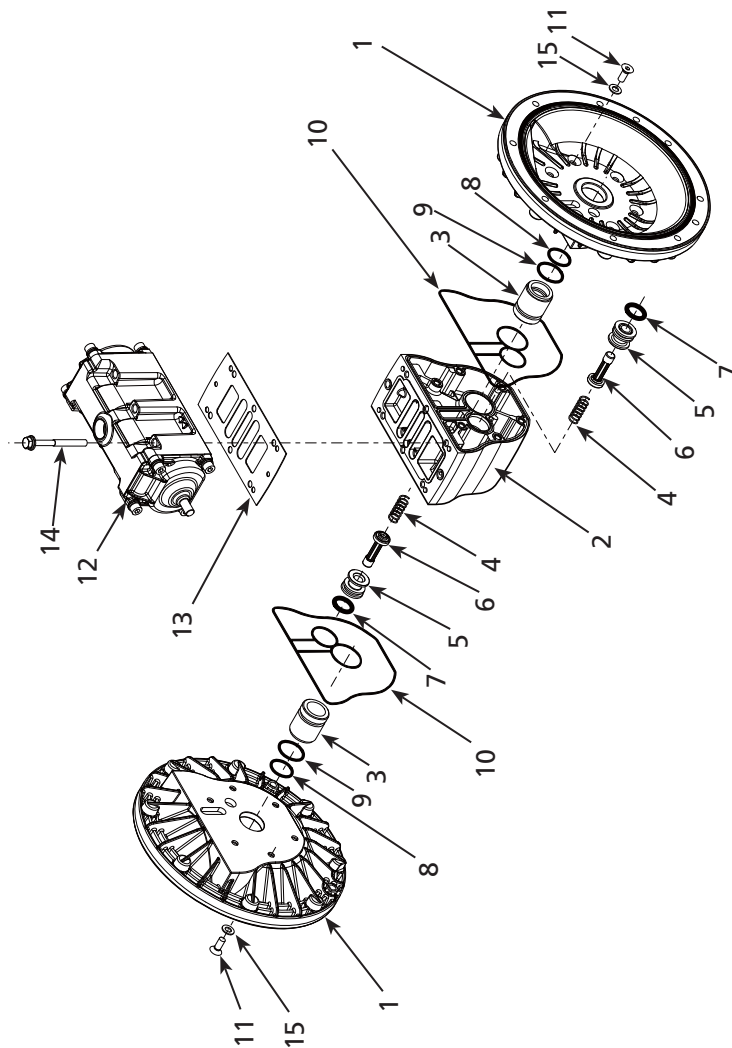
Illustration des pièces de réparation pour le corps Assemblée
